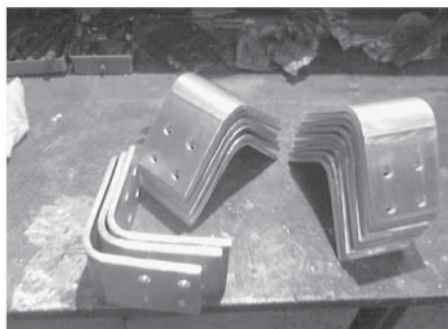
Переходники алюминий–медь, полученные сваркой взрывом
